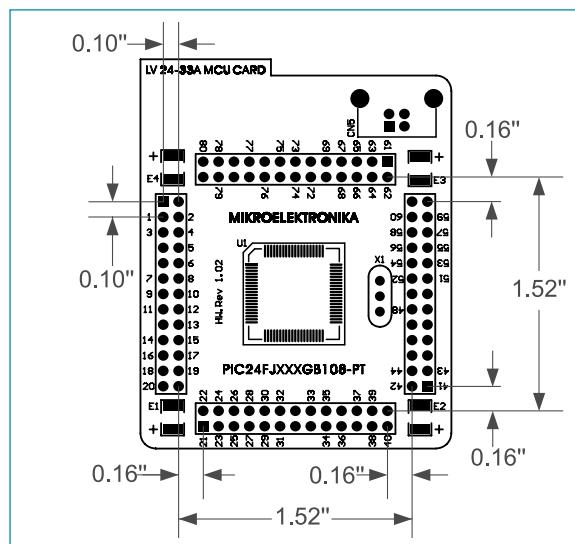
Dimensiones de la tarjeta MCU para la MCU Card 14
